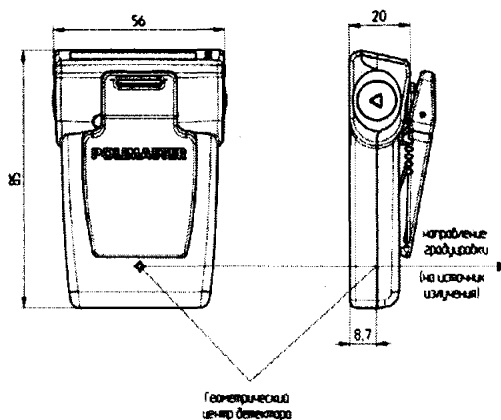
Габаритные размеры, расположение геометрического центра детектора и направление градуировки
